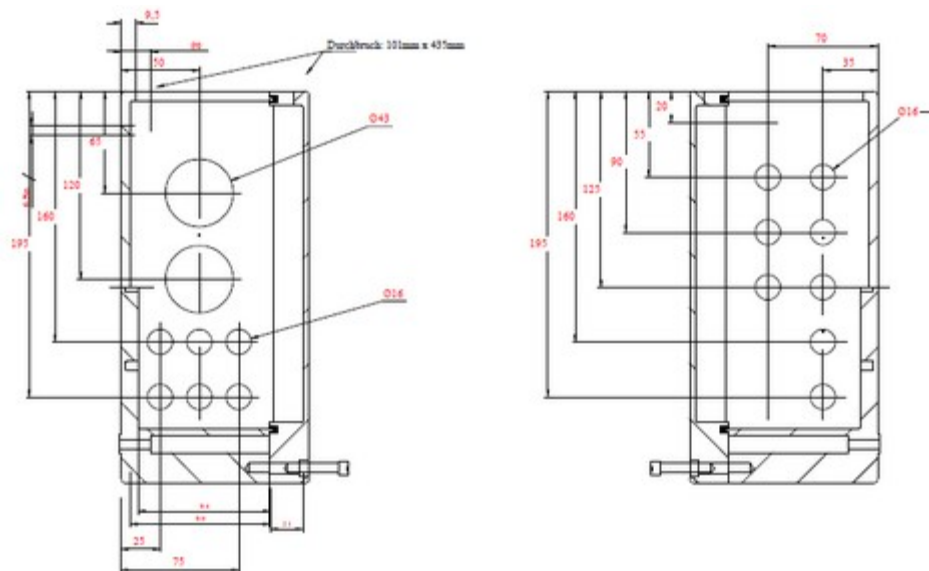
2: Kunststoff-Gehäuse IP67 für die Motorsteuerung (Seitenansicht)
